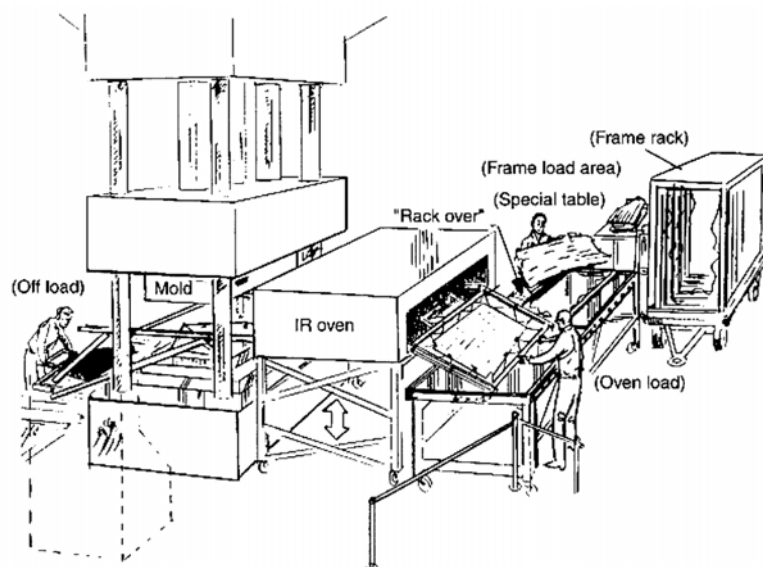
Chaîne de thermostamping [CAM 10].
